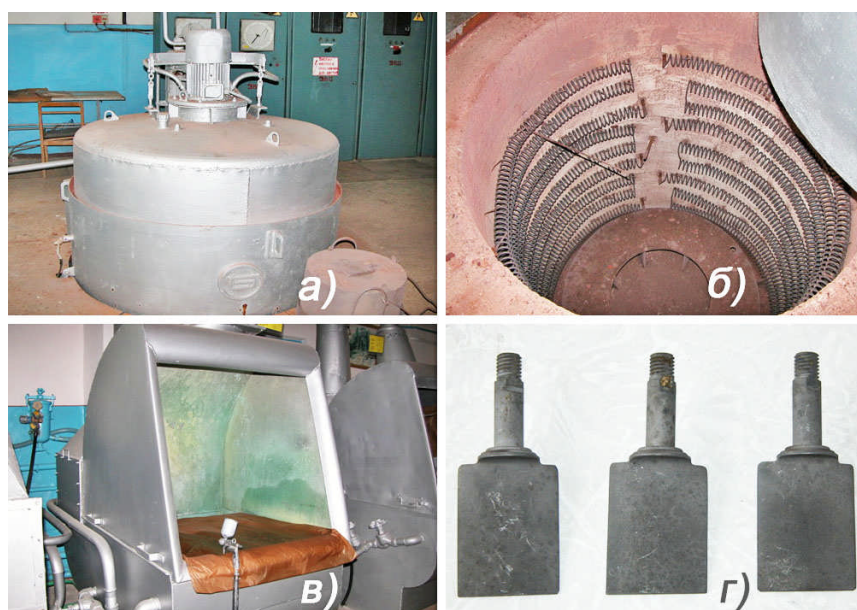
Оборудование для нанесения покрытий ДифА-СФ и Х-ДифА: а – внешний вид установки и загрузочного контейнера; б – загрузочная шахта; в – участок для нанесения фосфатного слоя; г – покрытие ДифА-СФ на лопатках компрессора
